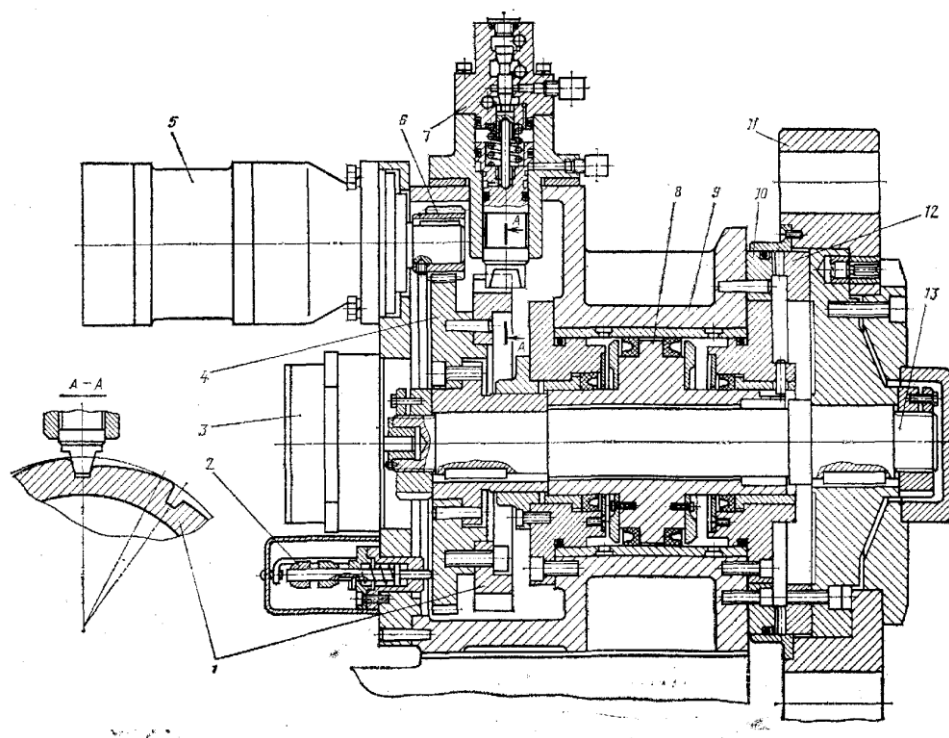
Конструкция гидрофицированной револьверной головки токарного станка
